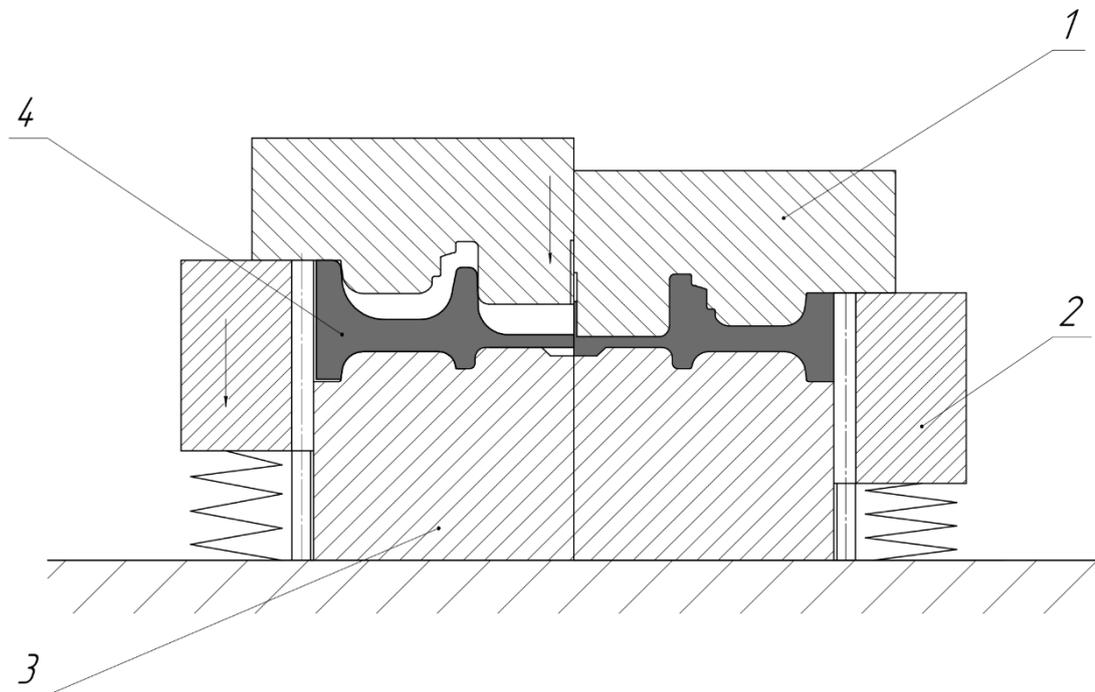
Схема штамповки (1 – верхний пунсон, 2 – плавающая матрица, 3 – нижний пуансон, 4 – поковка)
